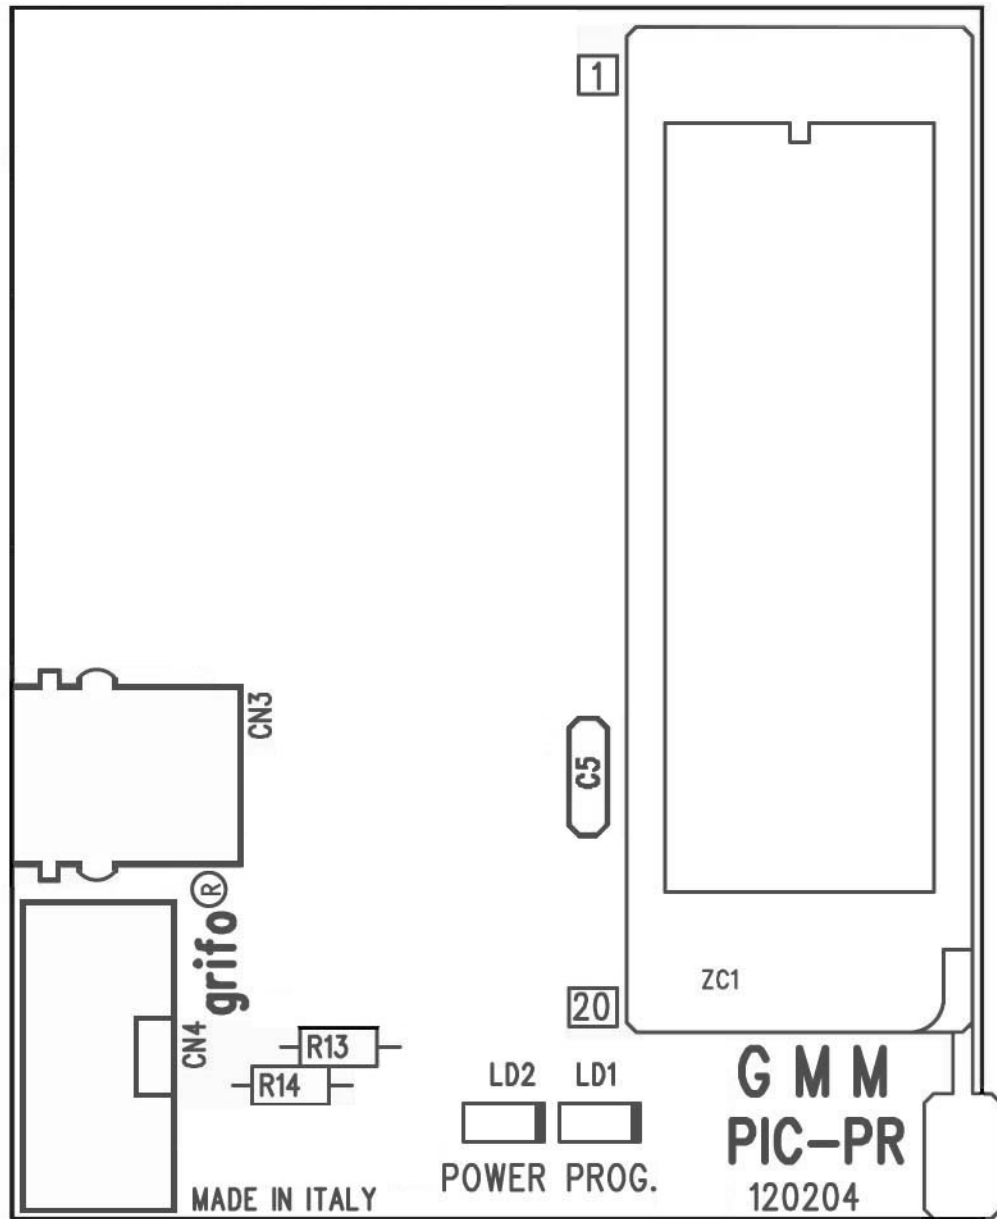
PIANTE COMPONENTI - VISTA LATO COMPONENTI
